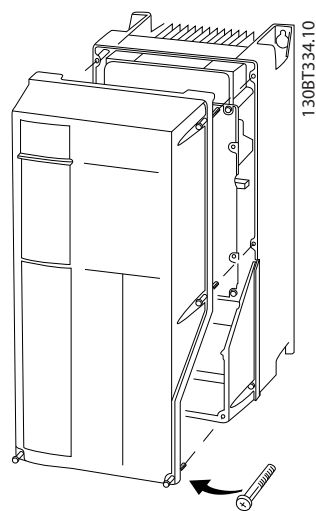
Acceso al cableado de las protecciones IP55 e IP66
